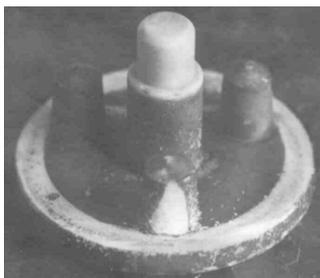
Износ рабочей поверхности клапана пульсатора
